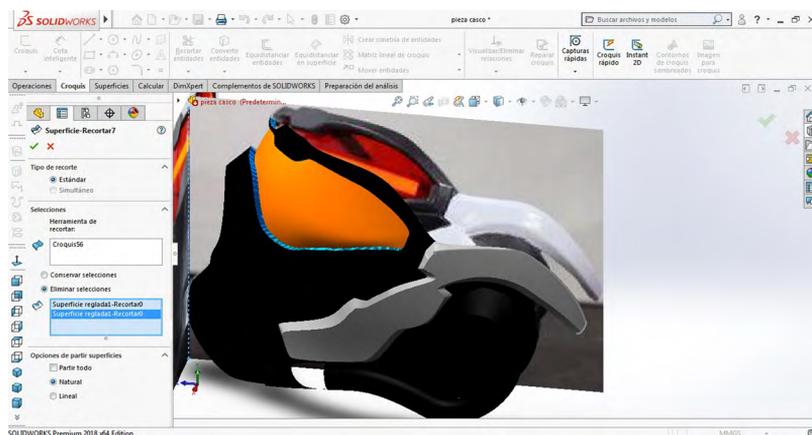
Mediante la opción de plano alzado y línea constructiva
